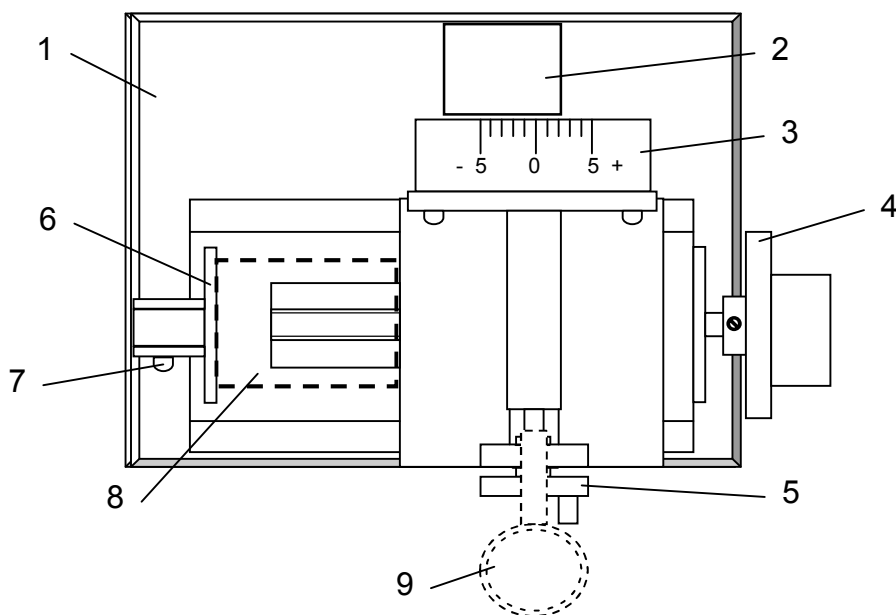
а. Установка датчика ВК-316ТР.01 на приспособление СП-20.
